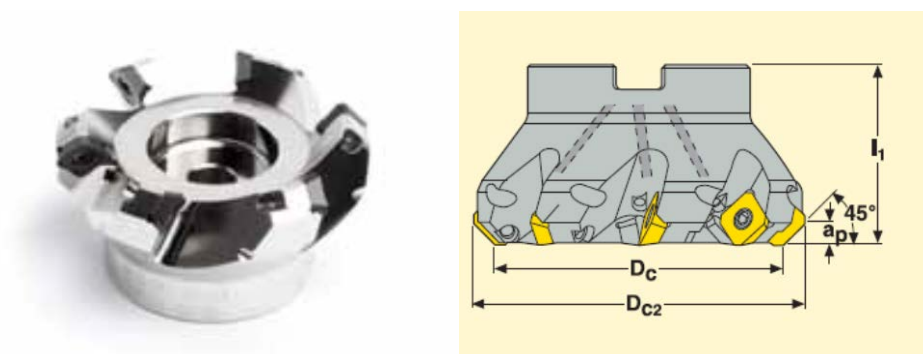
Фреза торцовая $\varnothing 100$ R217.53 – 0300-12-3А
